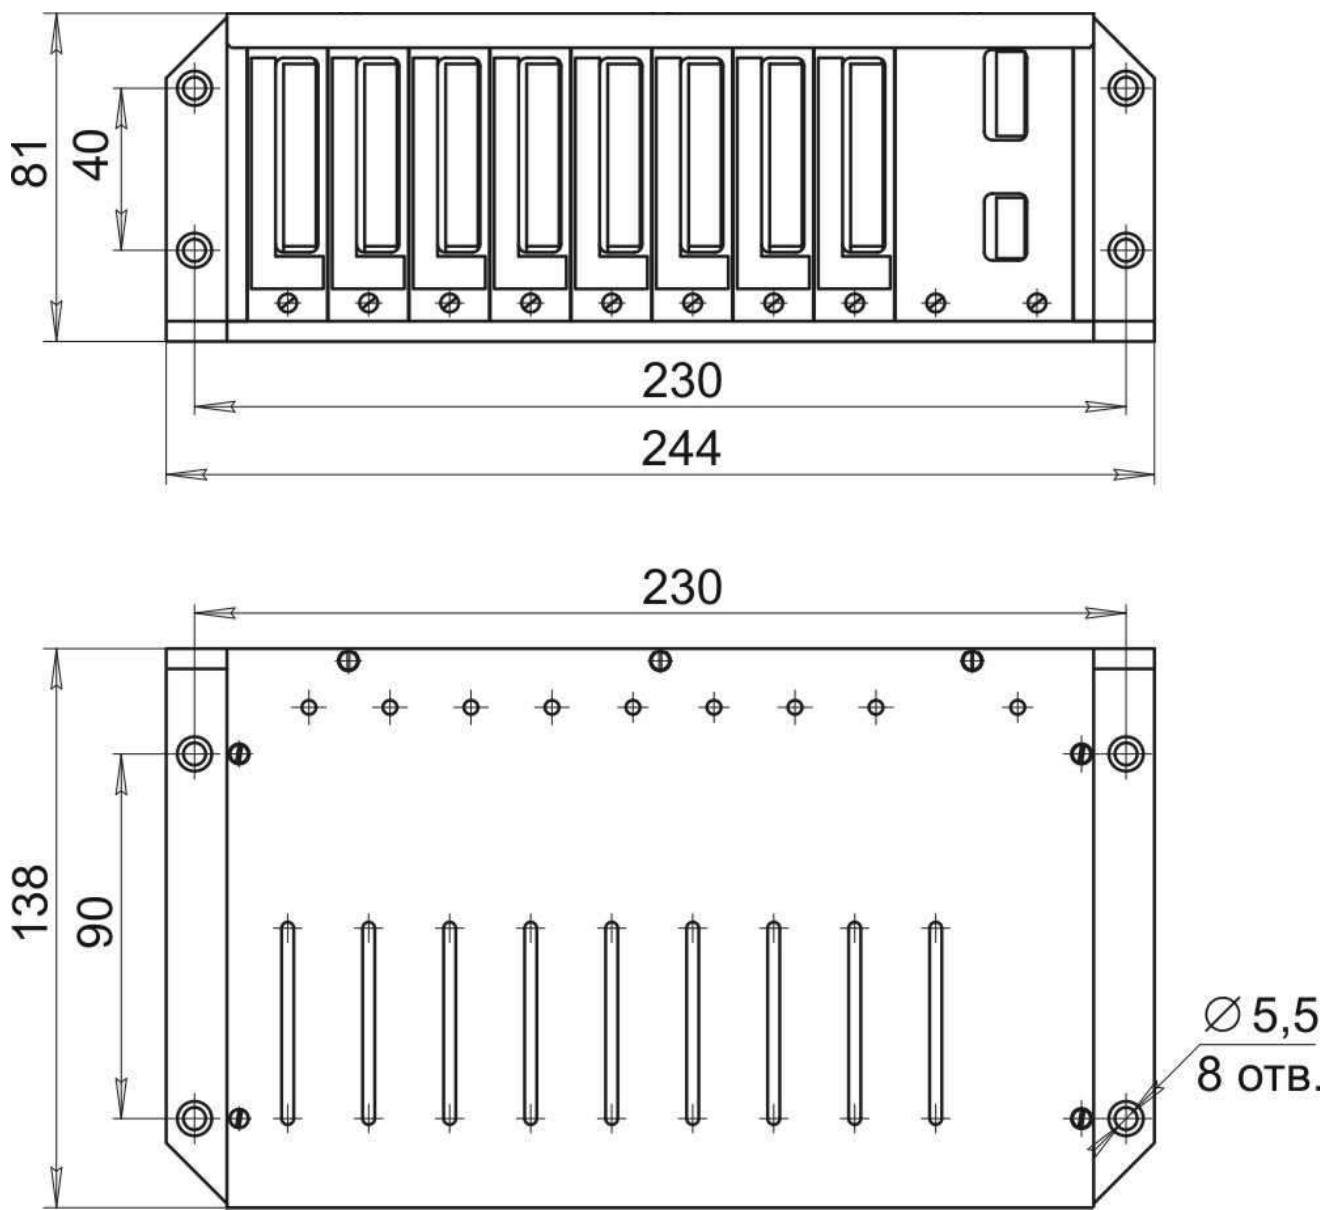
Габаритные и установочные размеры БМ-8
